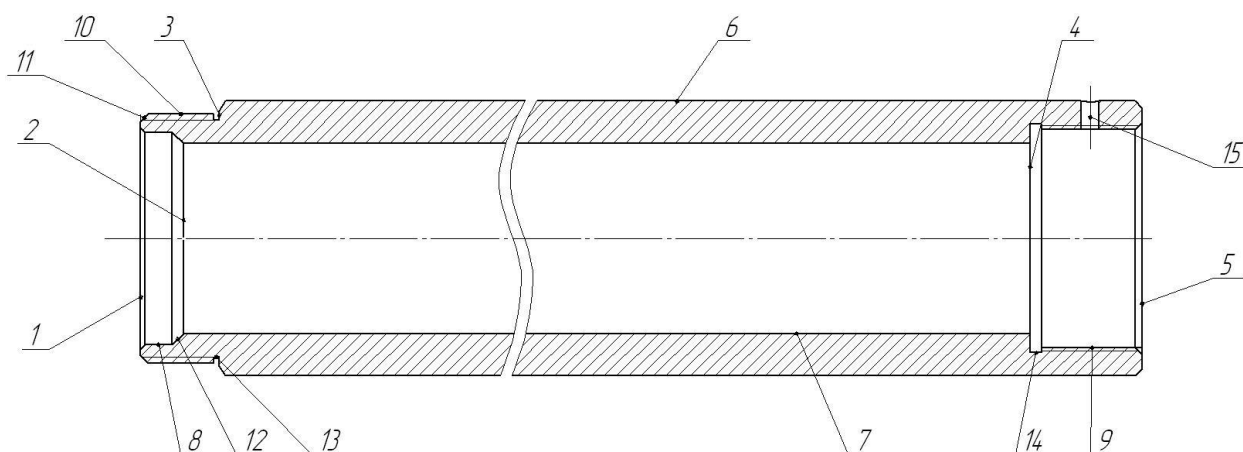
Эскиз корпуса с номерами поверхностей
